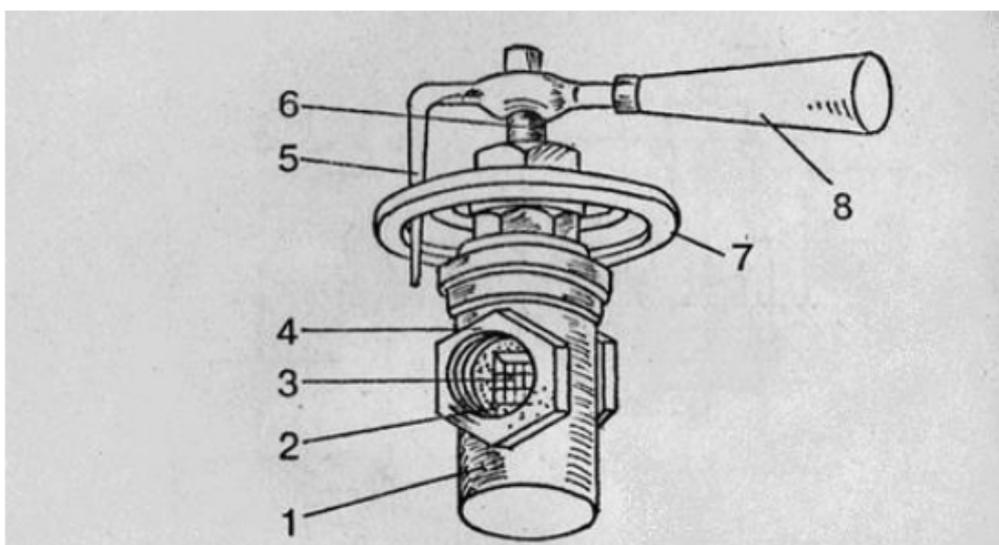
Кран двойной регулировки: 1 — корпус; 2 — полый бронзовый стакан ; 3 — боковое окошко; 4 — проход корпуса; 5 — упорный палец; 6 — шпиндель; 7 — розетка; 8 — рукоятка
